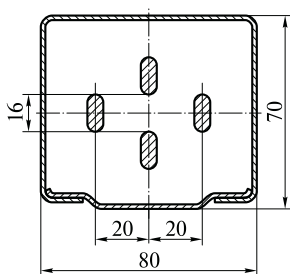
Поперечное сечение шинопровода ШРА4-100-44-1УЗ
